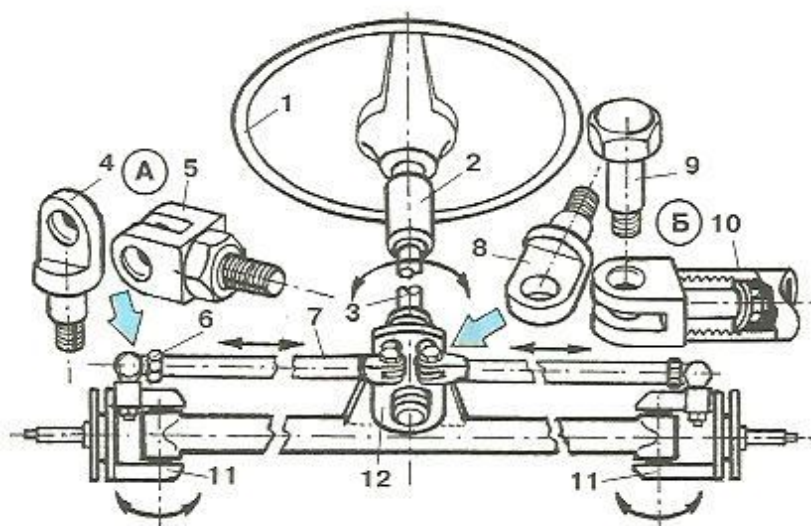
Механизм рулевого устройства: 1 — рулевое колесо; 2 — втулка рулевой колонки; 3 — рулевая колонка; А — детали шарнира цапфы: 4 — шарнир цапфы; 5 — шарнир тяги; 6 — контролочная гайка регулятора длины тяги; 7 — рулевая тяга; Б — детали шарнира рулевой сошки: 8 — шарнир сошки; 9 — ось шарнира; 10 — втулка вращения шарнира тяги; 11 — цапфа; 12 — сошка руля.
